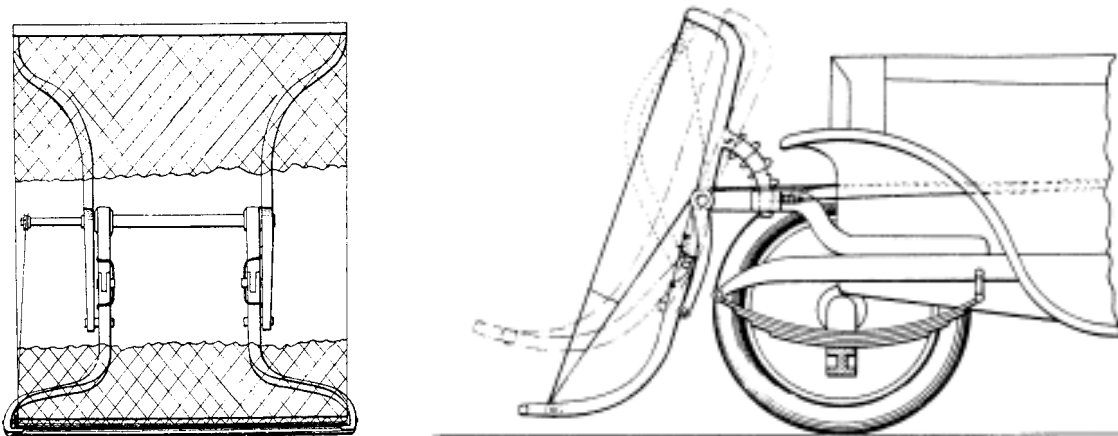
"Fangvorrichtung an Kraftfahrzeugen" aus dem Jahre 1924 [SIN24]
